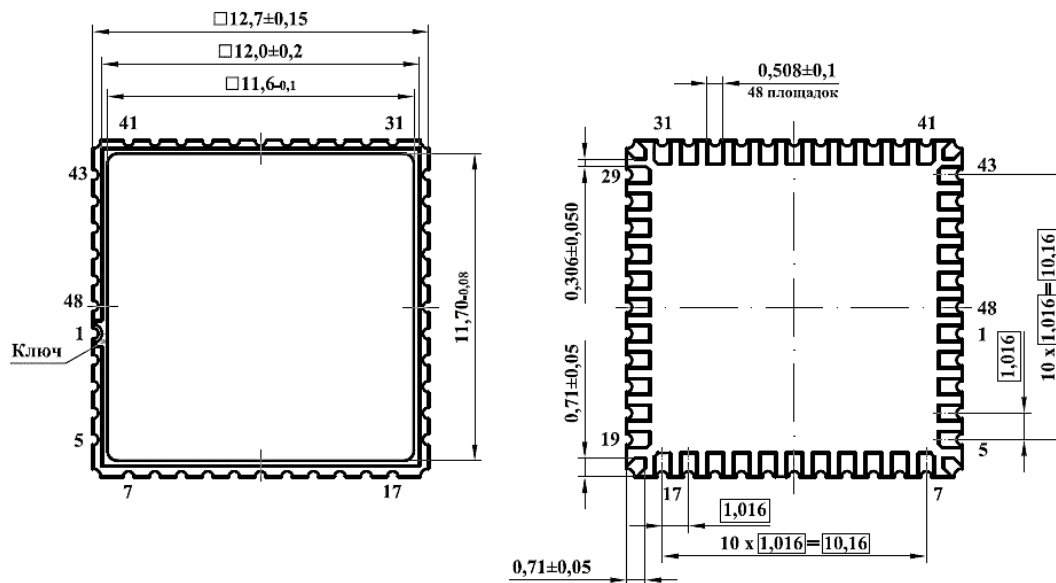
Габаритный чертеж корпуса 5142.48-A
